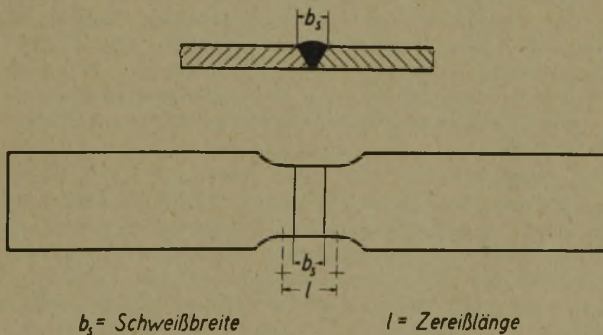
Schweißzerreiþstab (Schemakizze)
